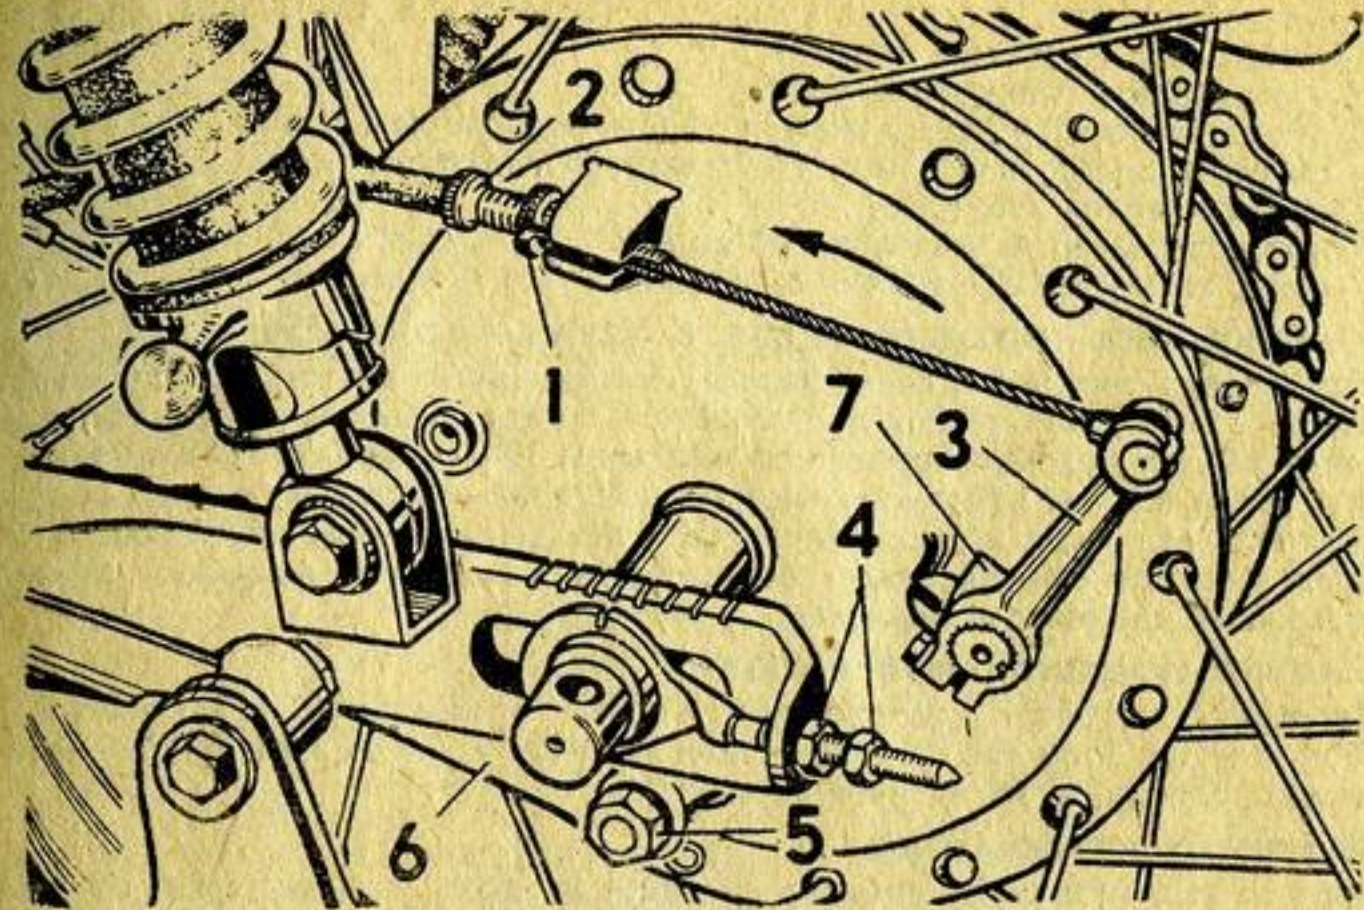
Снятие заднего колеса и регулировка тормоза заднего колеса
